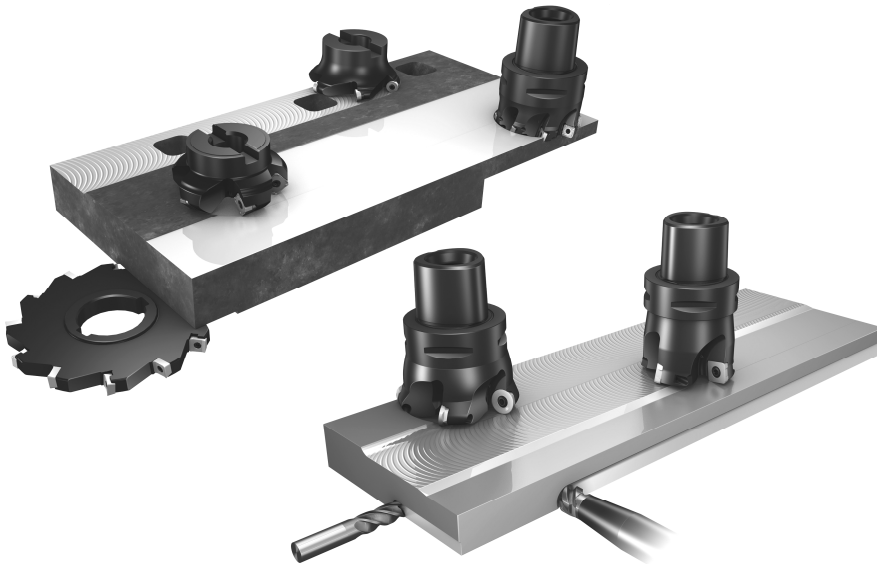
Використання фрез різної конструкції при торцевому фрезеруванні
